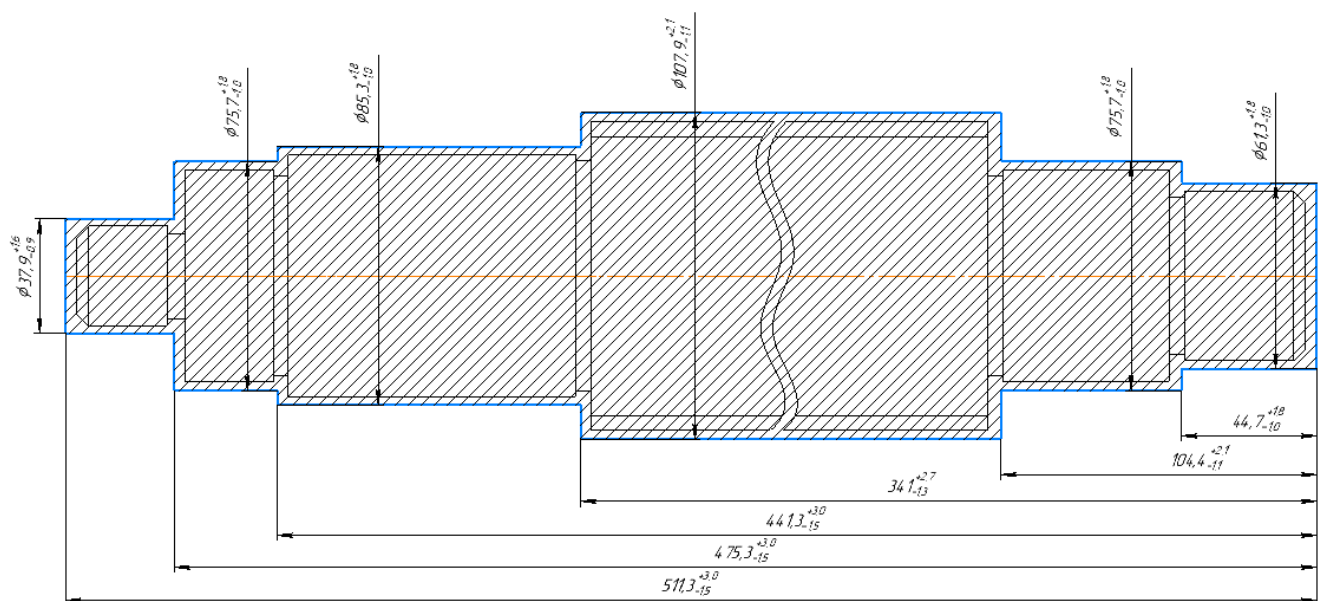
Ескіз заготовки виготовленої на ГKM
